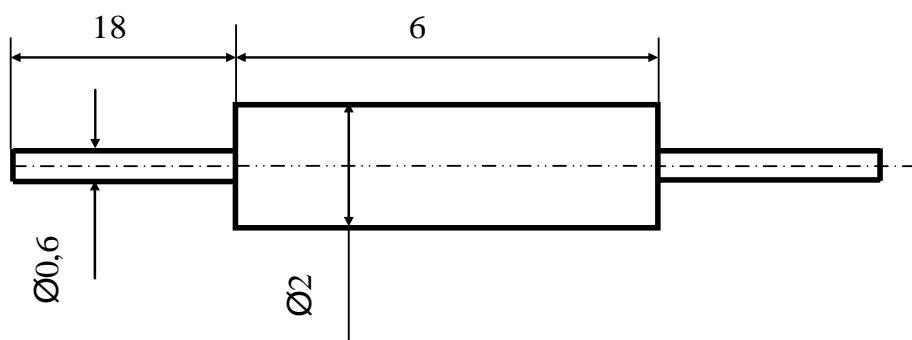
Внешний вид резистора МЛТ-0,125
